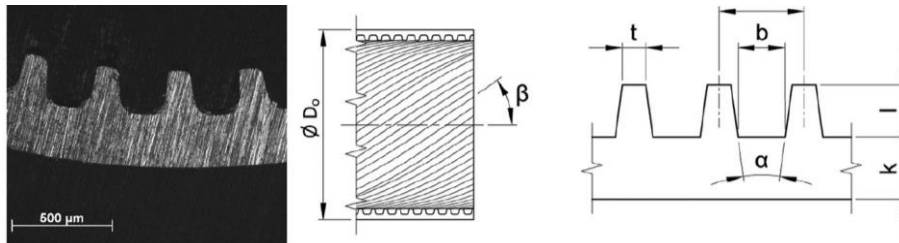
(gauche) Photographie de la section transversale d'un tube à ailettes hélicoïdales et (droite) schémas définissant les dimensions caractéristiques [215]
